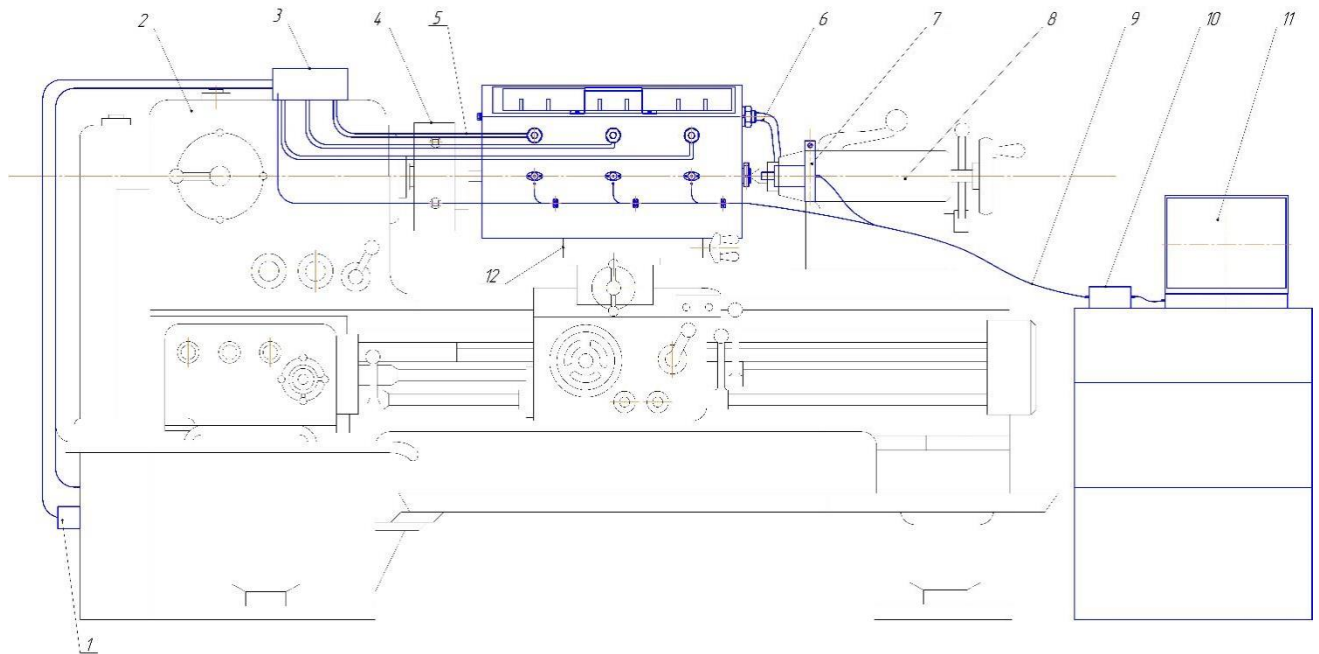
Установка для дослідження процесів зношування деталей машин: 1 – гідророзподільний клапан; 2 – токарно-гвинторізний верстат; 3 – гідророзподільник; 4 – трикулачковий патрон; 5, 6 – трубопровід; 7 – датчик оборотів; 8 – задня бабка; 9 – сполучні дроти; 10 – контролер; 11 – комп'ютер; 12 – супорт із установкою для випробувань.
